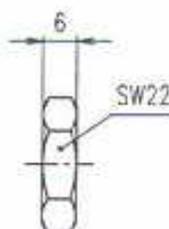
4) Fitting para cañerías de pilotaje 6 mm.
